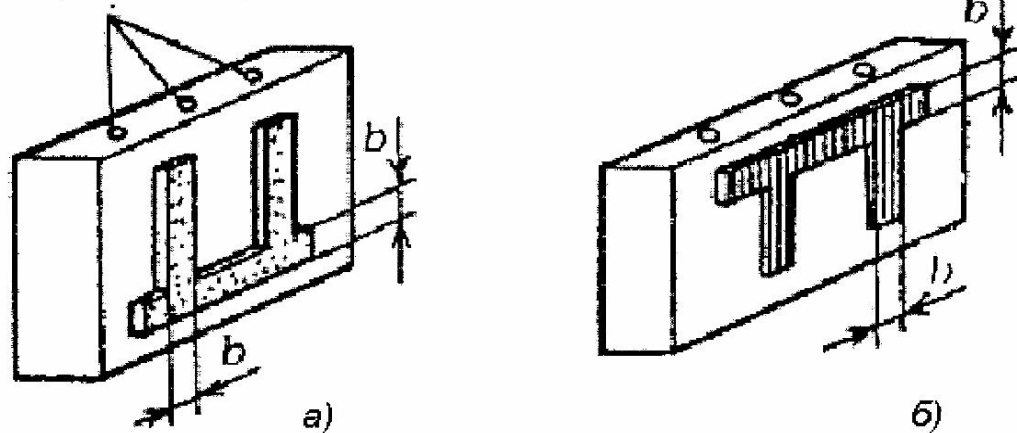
Плоскі плити для контактнo-теплового зварювання з гладкою(а) і рифленою (б) поверхнями зварного шва
